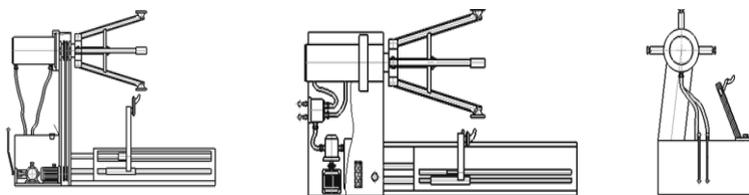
Стенд для монтажа и демонтажа шин колес грузовых автомобилей
